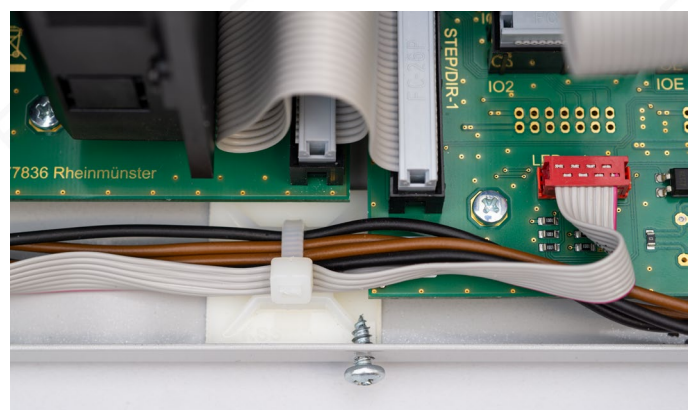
Schraube kann unbefestigte Kabel durchstechen.
